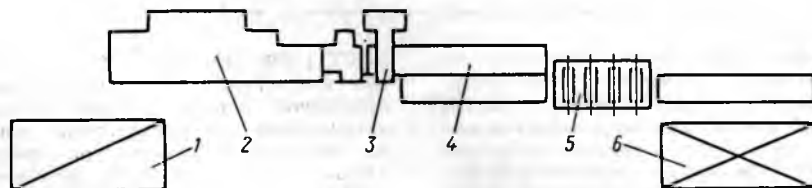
Схема участка изготовления продольных брусков, склеенных по сечению на зубчатый шип:
